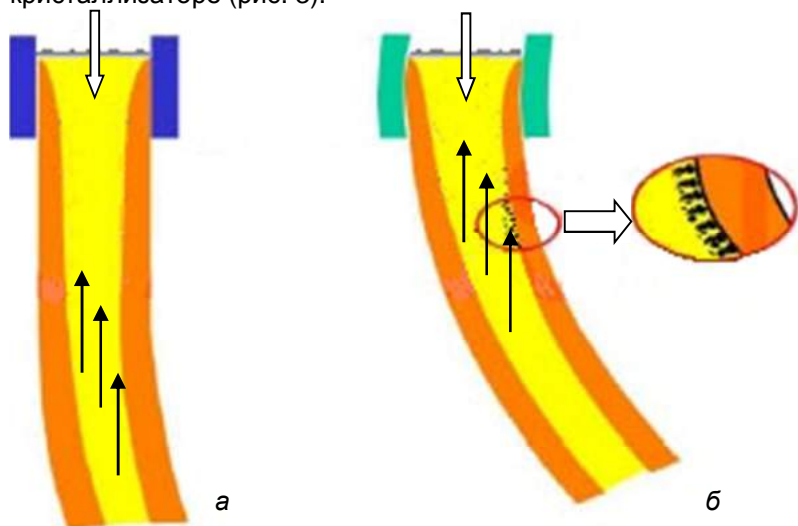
Схема удаления из лунки жидкого металла слябовой заготовки неметаллических включений при разливке стали на криволинейной МНЛЗ с вертикальным участком (а) и без него (б)
